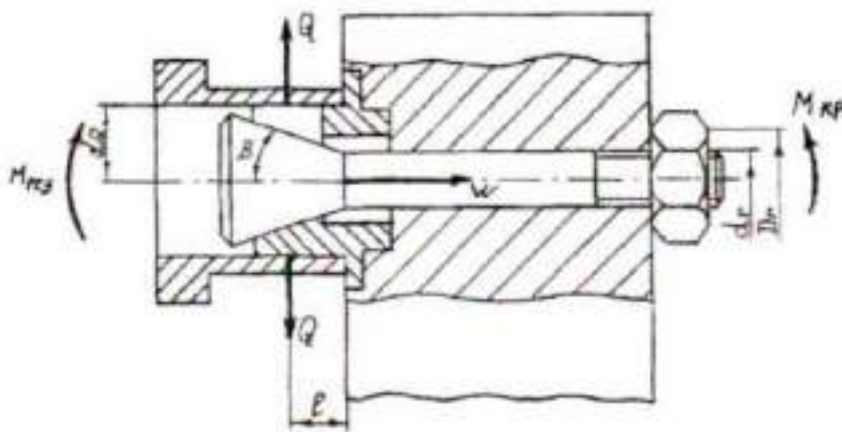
Расчетная схема для определения усилия зажима заготовки на станке
